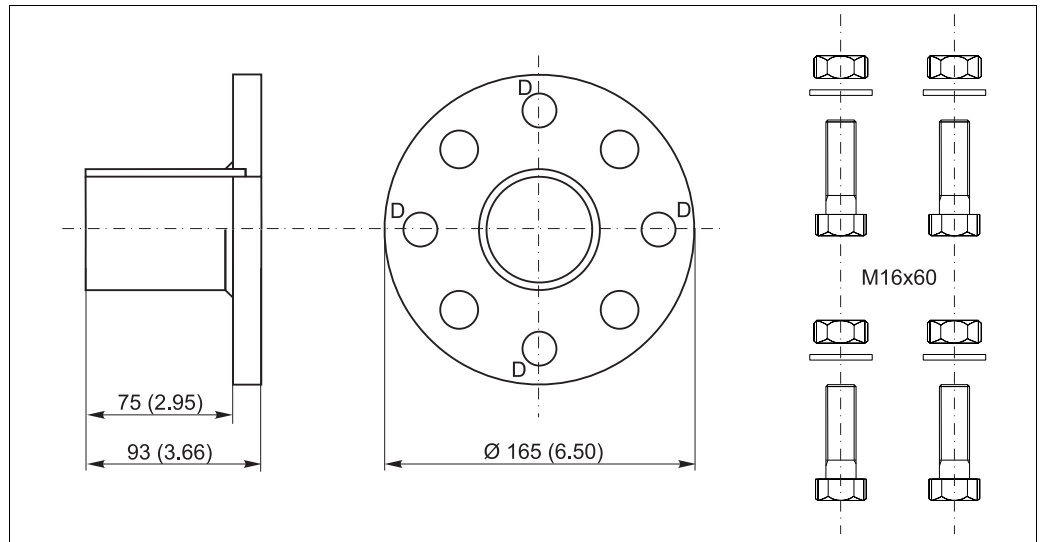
Einschweißstutzen, Abmessungen in mm (inch)
